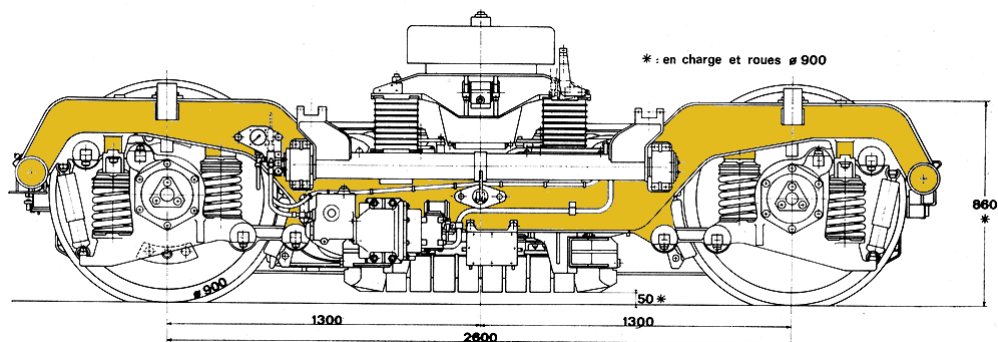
vue de face du dessin d'ensemble d'un bogie de TGV
